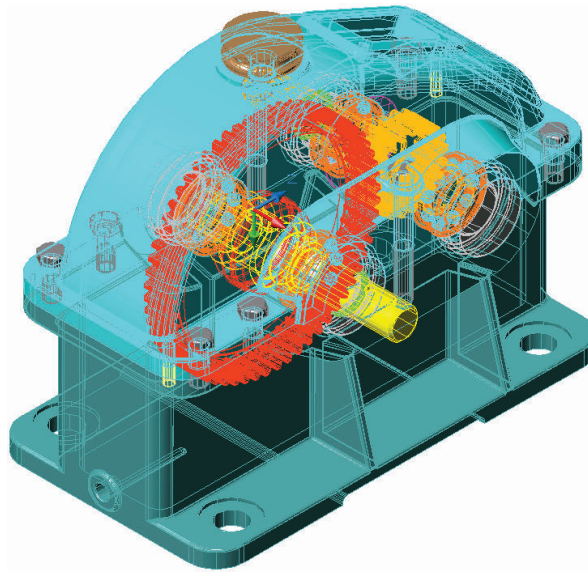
Загальний вигляд тривимірної моделі редуктора
